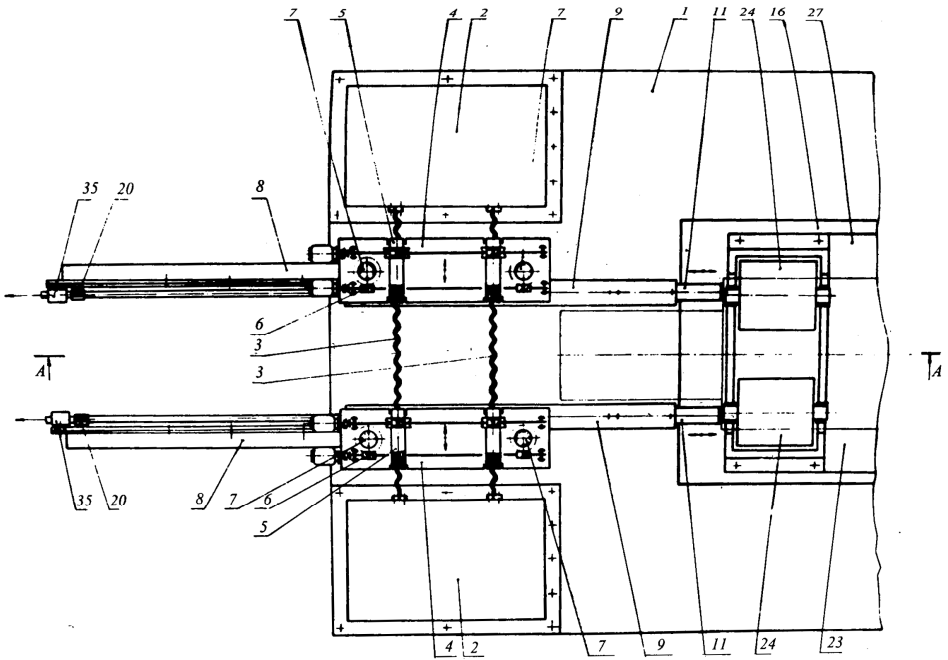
Кінематична схема верстату «Дуга-13» (вид в плані)
